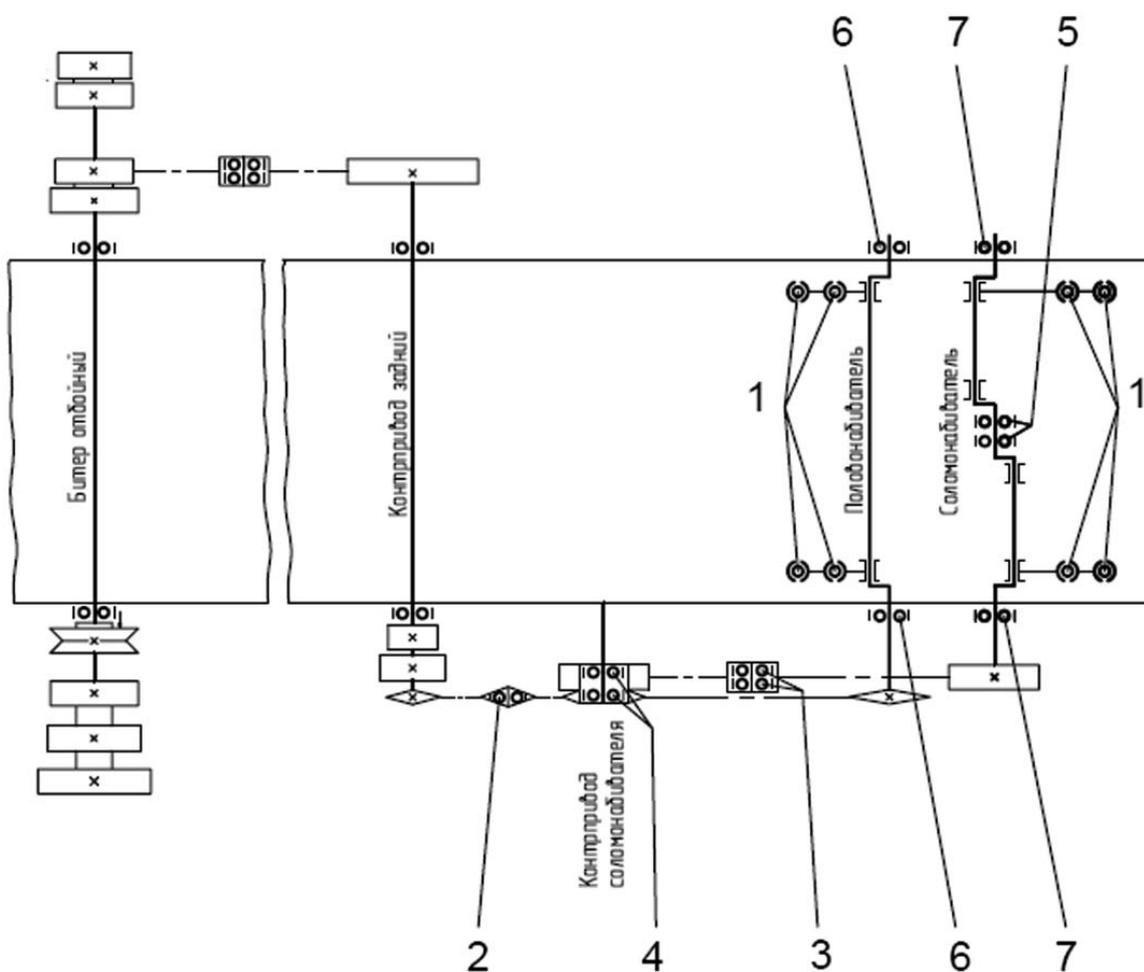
Схема расположения подшипников копнителя комбайна
